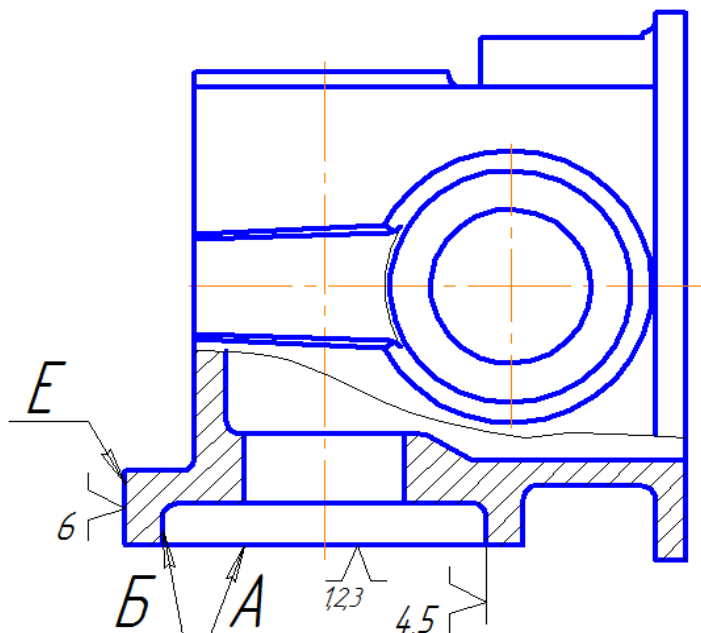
Черновые базы предлагаемого тех. процесса
